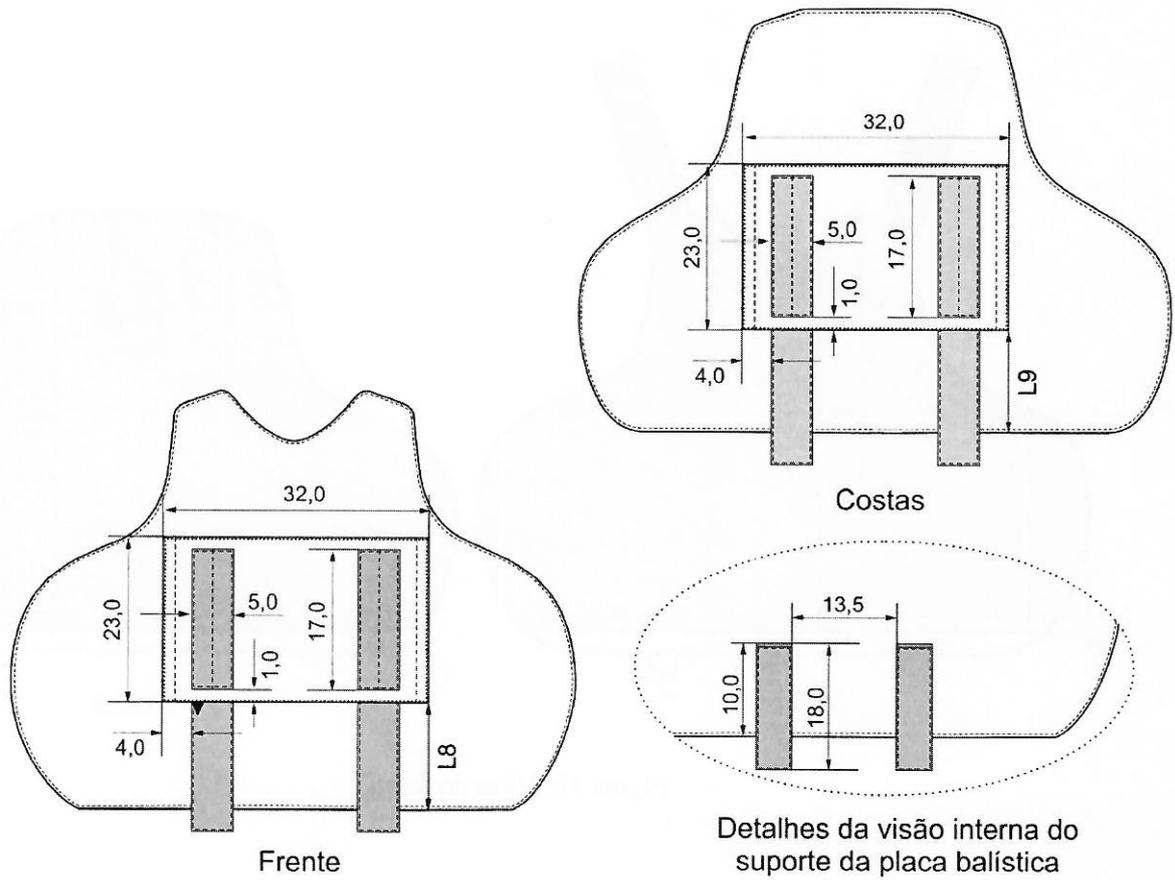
Vista do suporte interno de placa rígida (Medidas em cm)
